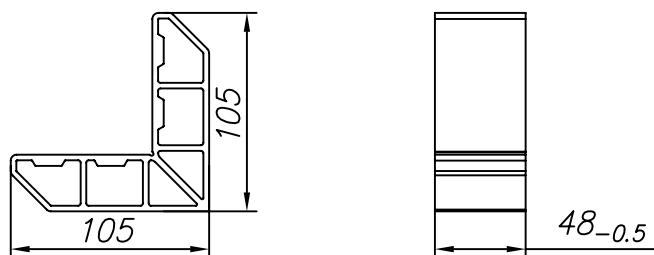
Изготовление соединителя углового FLGU.400.0910
